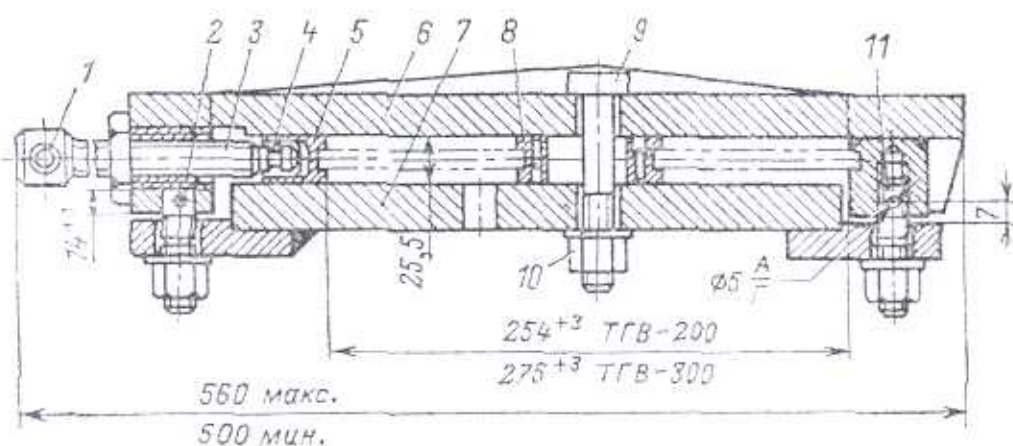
Приспособление для пайки головок статоров генераторов ТГВ-200, ТГВ-300:
